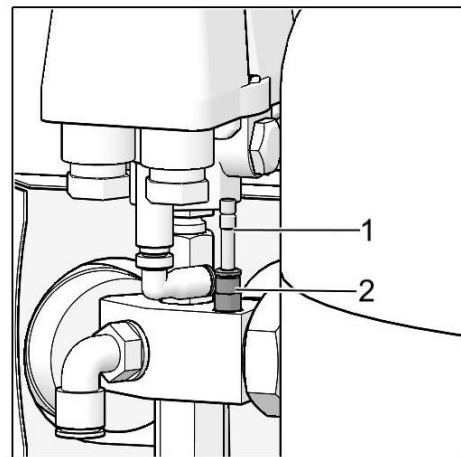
Verbinden des Gehäuse-Druckmessers mit dem Kompressor
